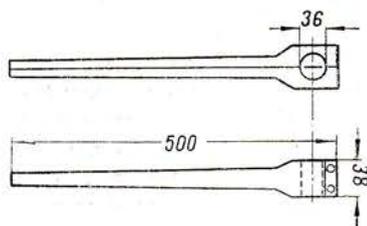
Обжимка для шлифовки шейки коленчатого вала
